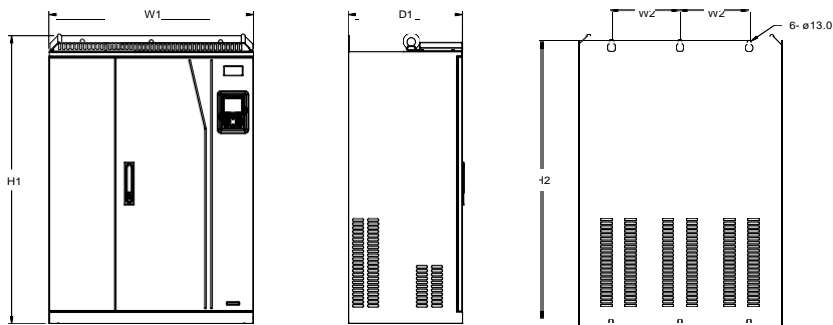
Схема настенного монтажа ПЧ напряжением 380 В, мощностью от 220 до 315 кВт
